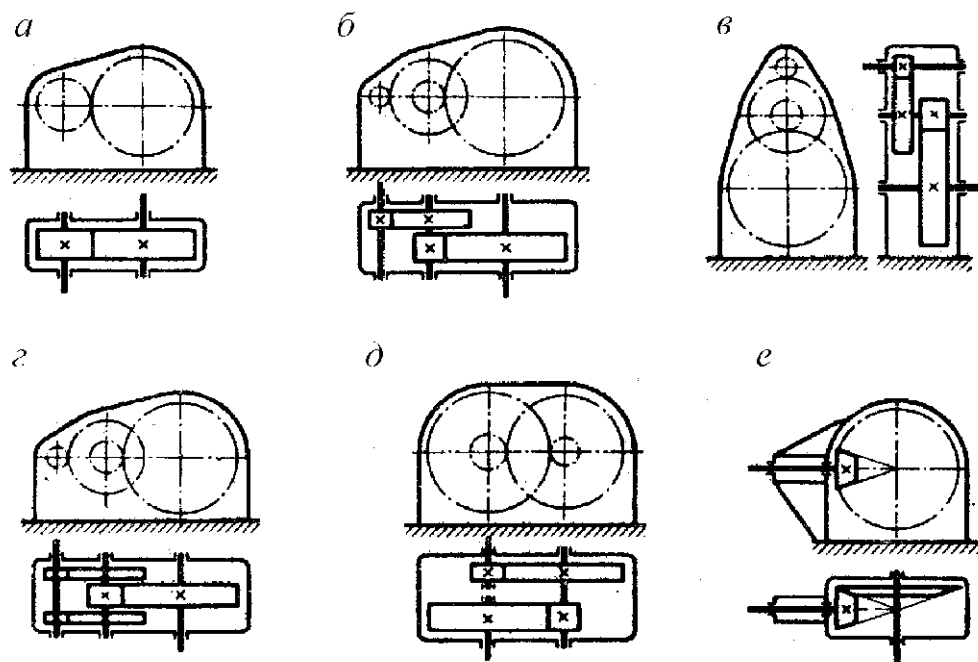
Кинематические схемы зубчатых редукторов
